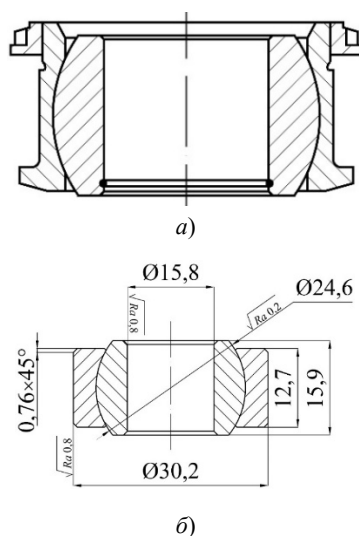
Конструкция сферических шарнирных узлов: *а* — наружная обойма с фланцем; *б* — наружная обойма без фланца [1]
